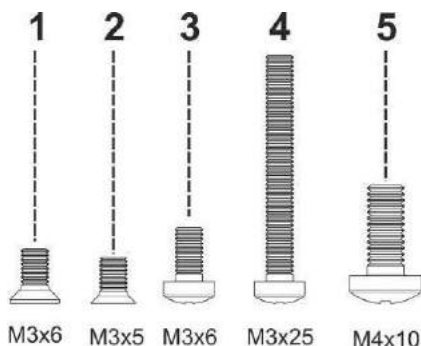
Типы болтов для сборки TAU-24.IP/TAU-16.IP
